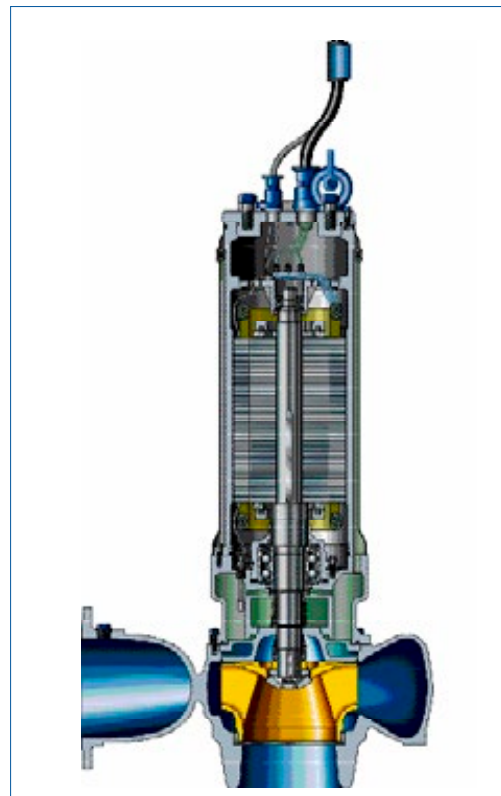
Plan en coupe d'une KRT > 60 kW
